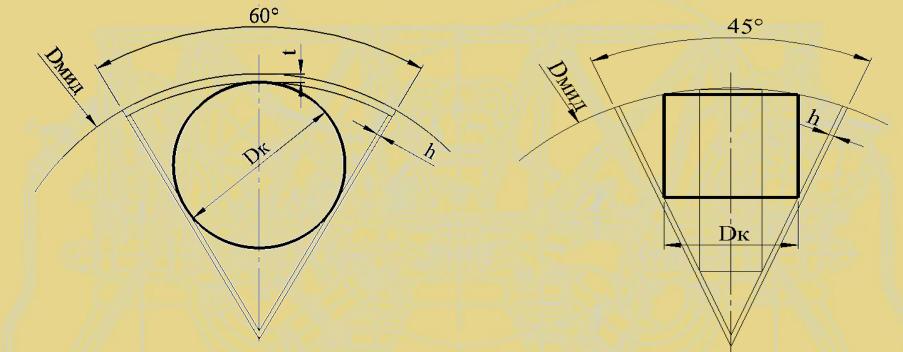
Предварительная прорисовка поперечного заполнения корпуса ЛА
